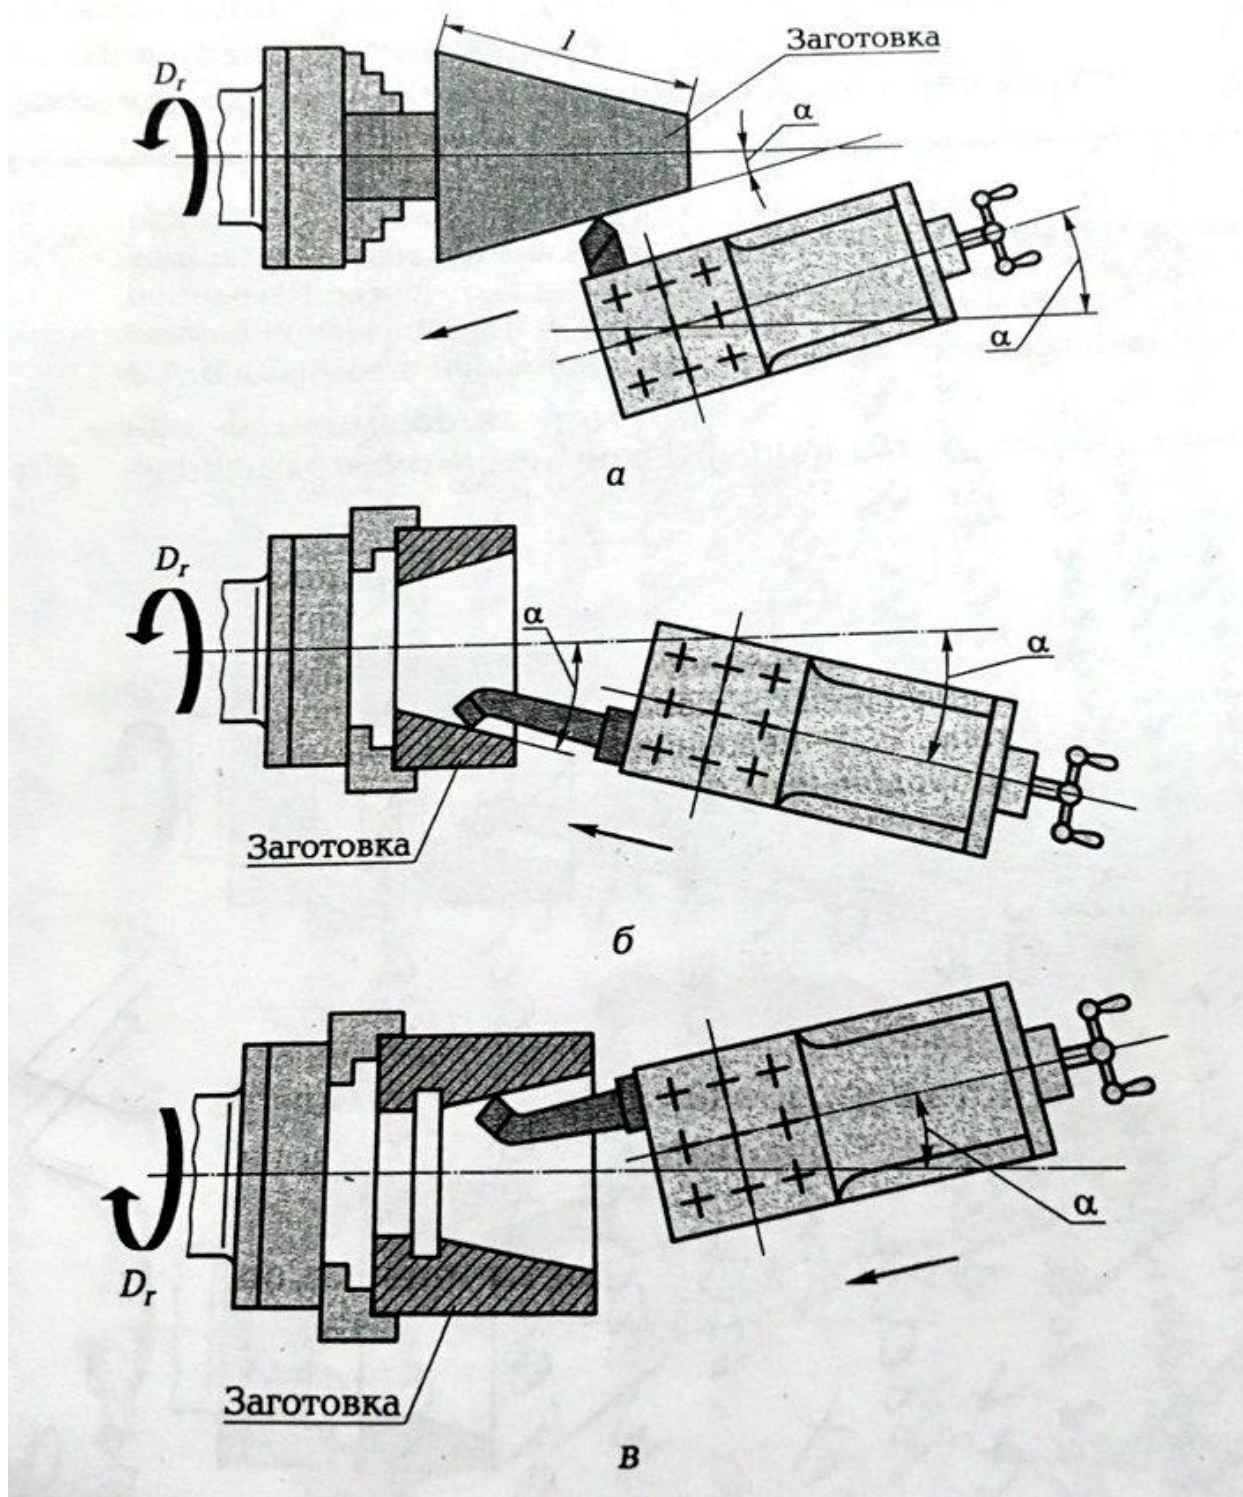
Обработка конических поверхностей путем поворота верхней части суппорта:
